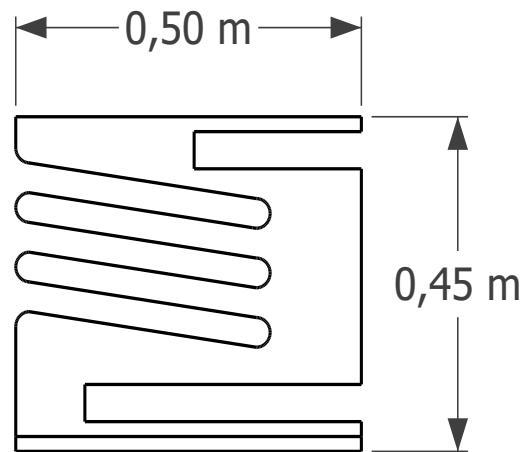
Autoría Jose Cruz. Planta velador 1
